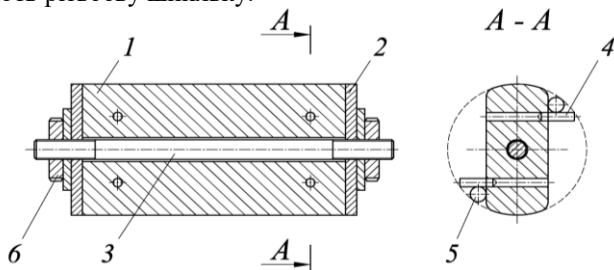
Технологічне пристосування для виготовлення каркасу секції шарнірного валу: 1 – основа; 2 – торцева шайба; 3 – різьбова шпилька; 4 – фіксуєючий палець; 5 – стержень; 6 – гайка
